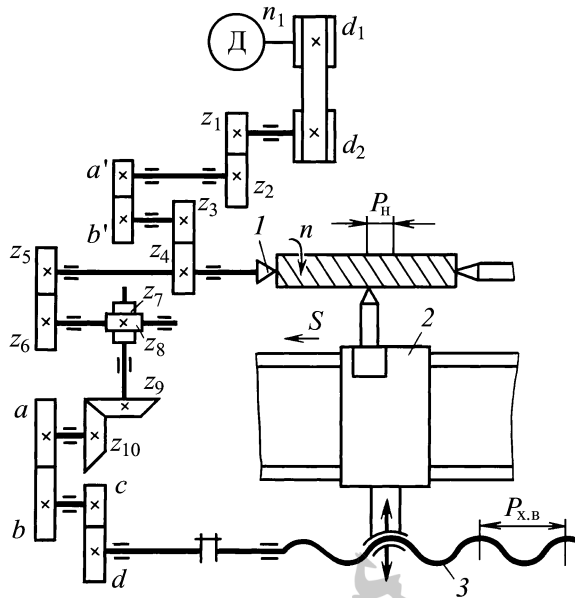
Кинематическая схема токарно-винторезного станка
